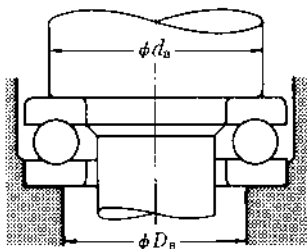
Диаметры поверхности опора для упорных шарикоподшипников
